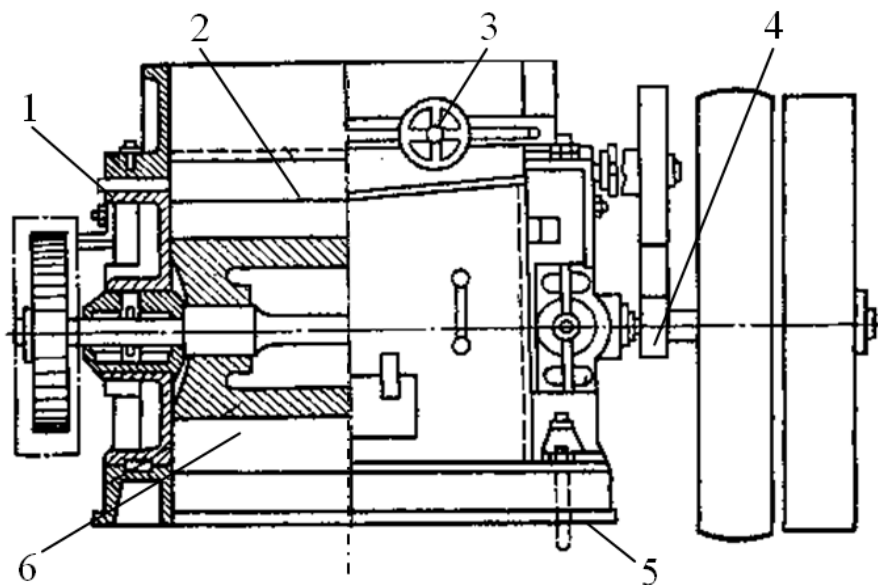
Однопарна двовальцьова дробарка: 1 – станина; 2 – живильний валик; 3 – гвинт регулювального шибера валика; 4 – вісь нерухомого валка; 5 – плита; 6 – рухомий валок.
